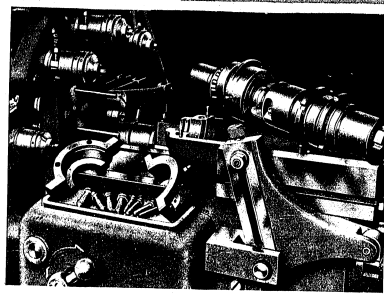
AUSGEBAUTER SPINDEL DER DREHMASCHINEN BP-U7 UND BP-U12
